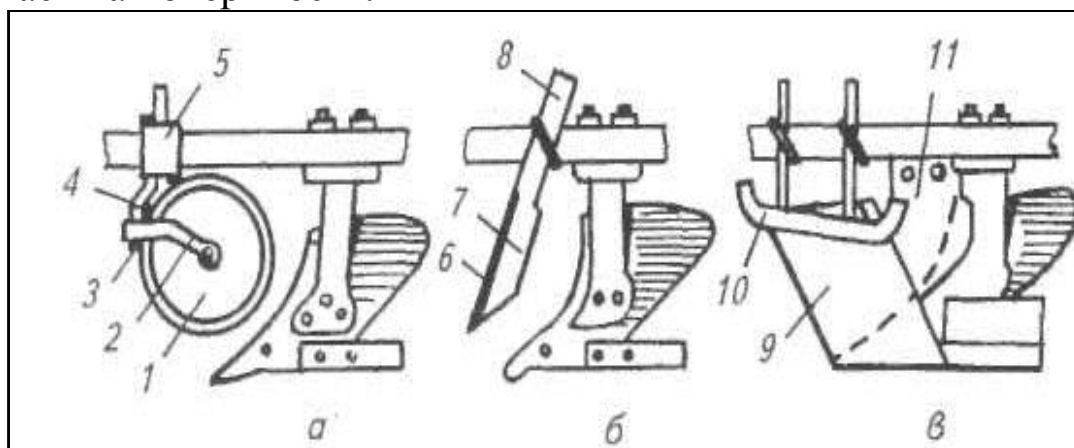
Ножи плугов: а – корпус плуга с дисковым ножом; б – корпус плуга с черенковым ножом; в – корпус болотного плуга с плоским ножом и опорной лыжей; 1 – диск; 2 – вилка; 3 – корончатая гайка; 4 – ось; 5 – накладка; 6 – лезвие черенкового ножа; 7 – спинка; 8 – черенок; 9 – плоский нож; 10 – лыжа; 11 – опорная пластина
